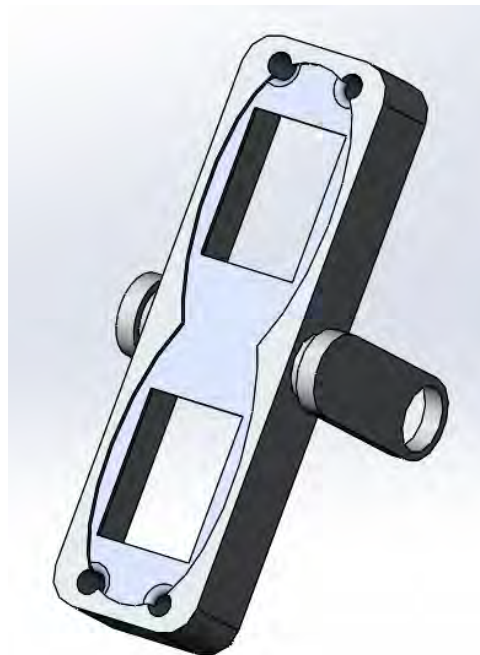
Зовнішній вигляд нижньої частини корпусу
